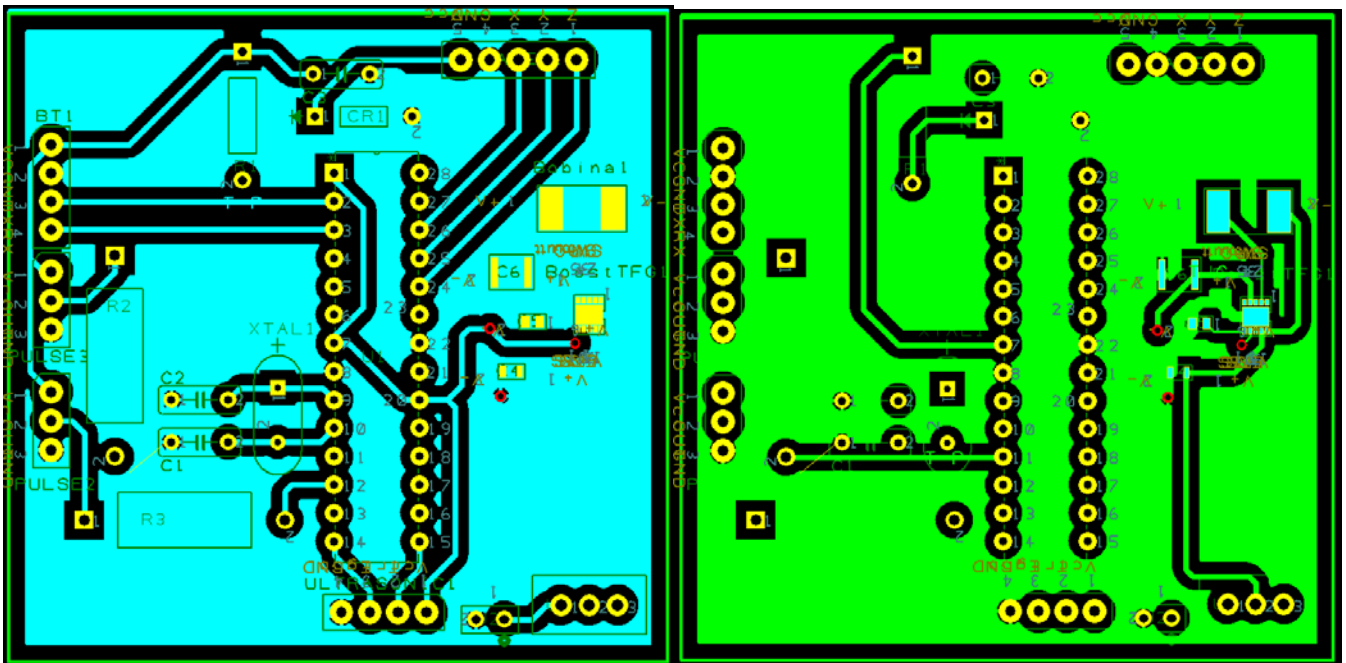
Caras TOP y BOTTOM de la placa del traje del bailarín
